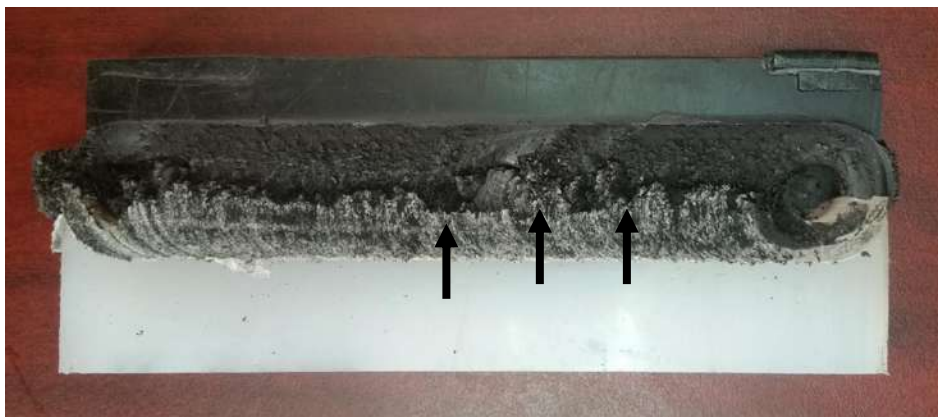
FSW de placas de ABS y polipropileno (defectos de soldadura).
